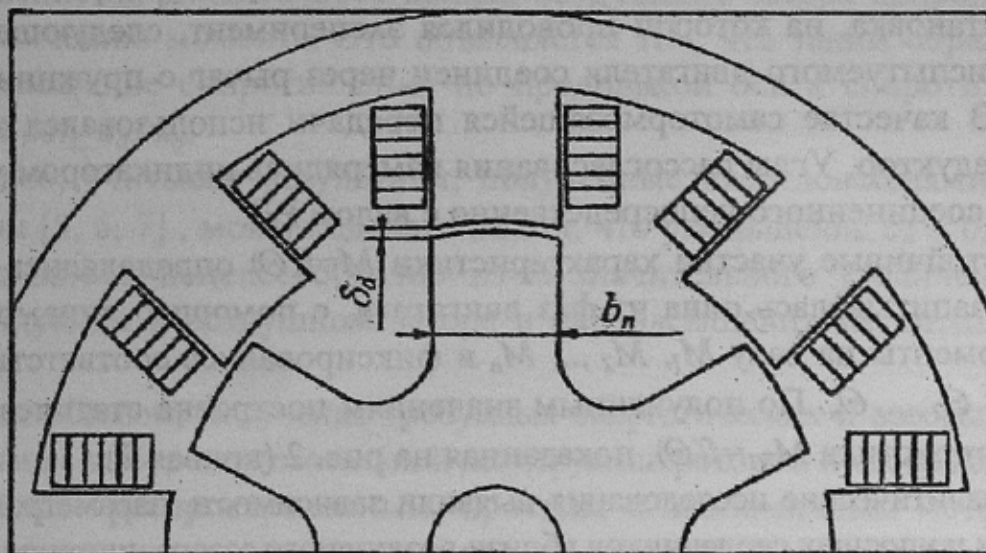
Схема конструкции разработанного двигателя (полюса с параллельными стенками)
